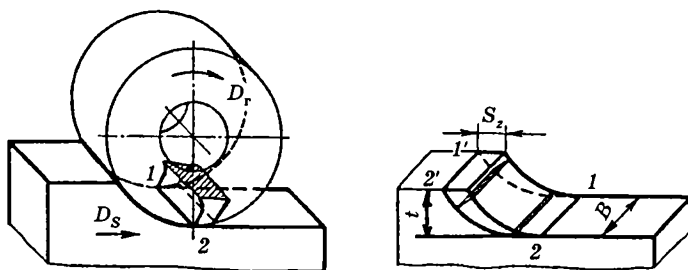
Движение фрезы и заготовки, параметры срезаемого слоя
